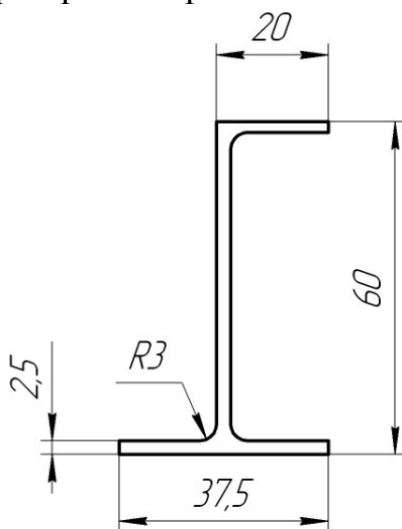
Сечение заготовки шпангоута, получаемой фрезерной обработкой на станке с ЧПУ
